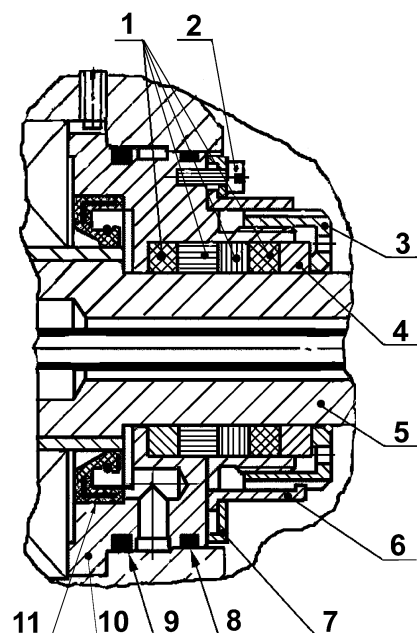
Уплотнение вала ступени высокого давления 1 – кольцо уплотнительное из набивки; 2 - винт; 3 – гайка; 4 - кольцо; 5 – вал; 6 - втулка стопорная; 7 – прижимное кольцо; 10 – корпус; 11 – манжета; 8, 9 – кольца уплотнительные.
